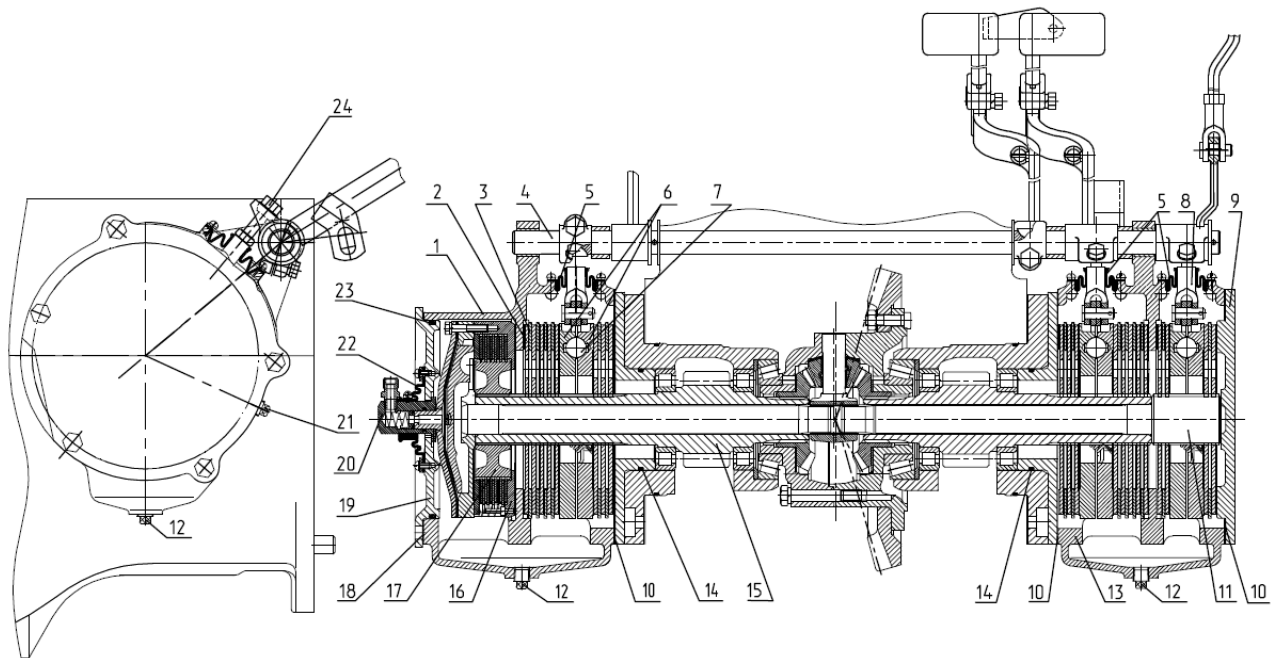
Регулировка управления стояночным тормозом
